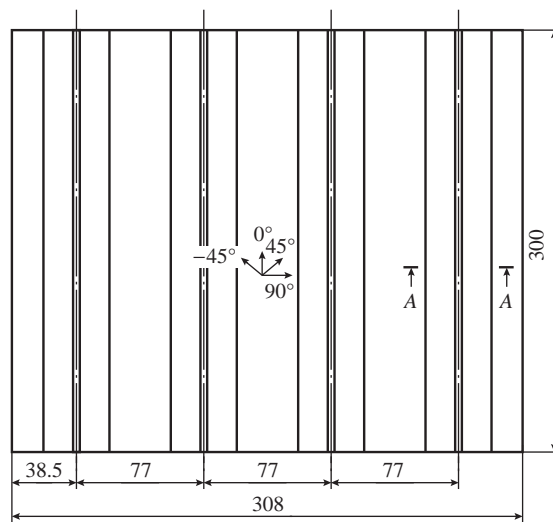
缝合复合材料 T 型加强板平面尺寸 (mm)
